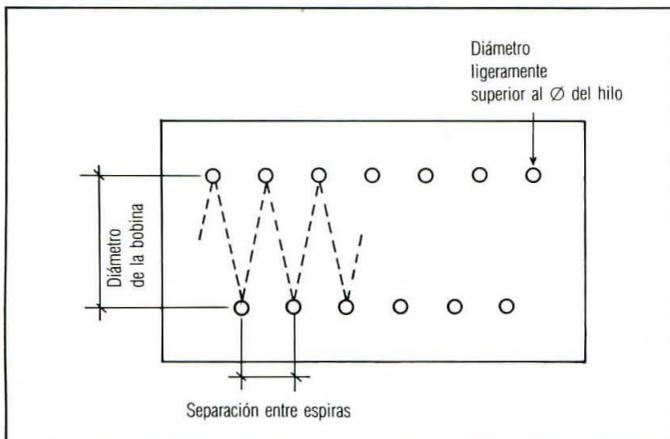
Disposición de los taladros en la placa para el montaje de la bobina.
